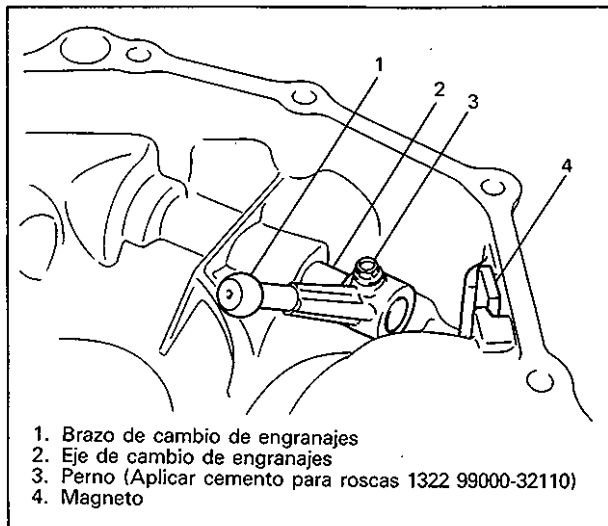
A-42 Instalación del brazo de cambio de engranajes
